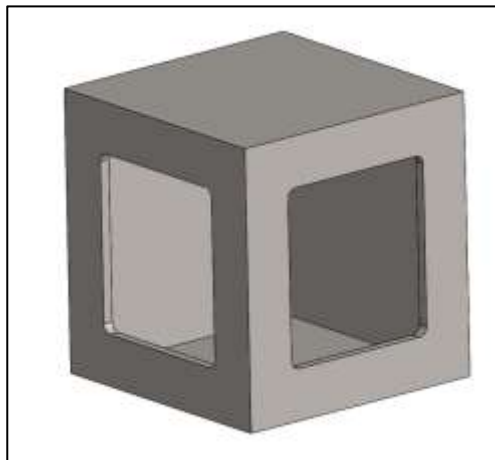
Cámara con plancha de 1.5mm, sin refuerzo
